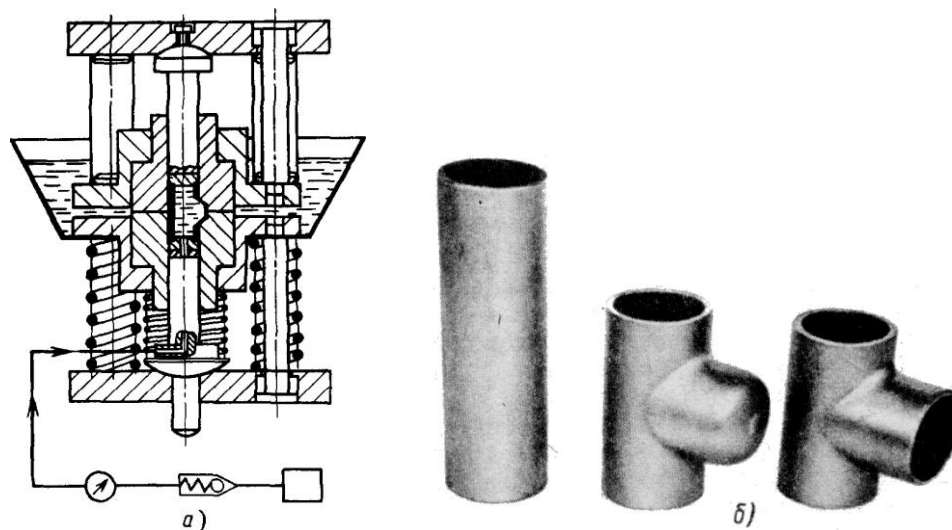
Штамп для изготовления тройника из трубчатой заготовки (а) и технологические переходы изготовления тройника (б)
